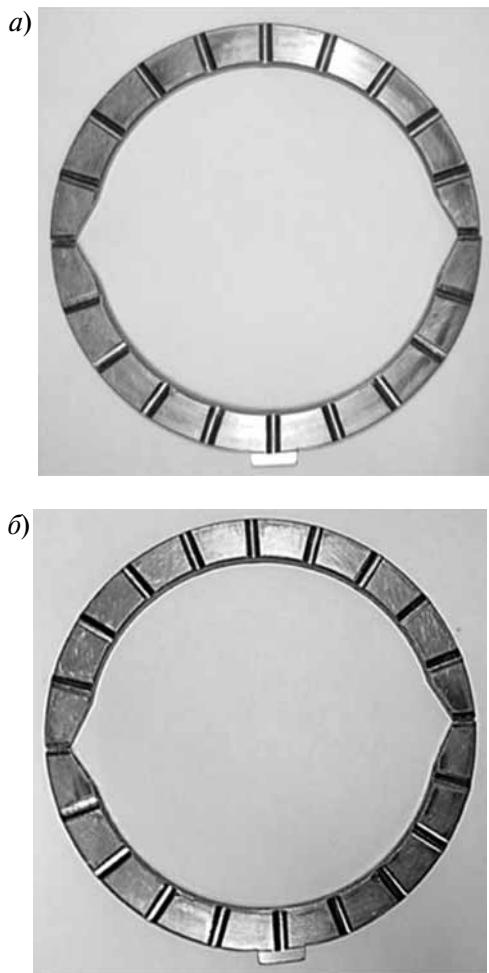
Фотоснимки опытных верхних и нижних полуколец переднего (а) и заднего (б) осевых подшипников коленчатого вала после приемо-сдаточных моторных испытаний
